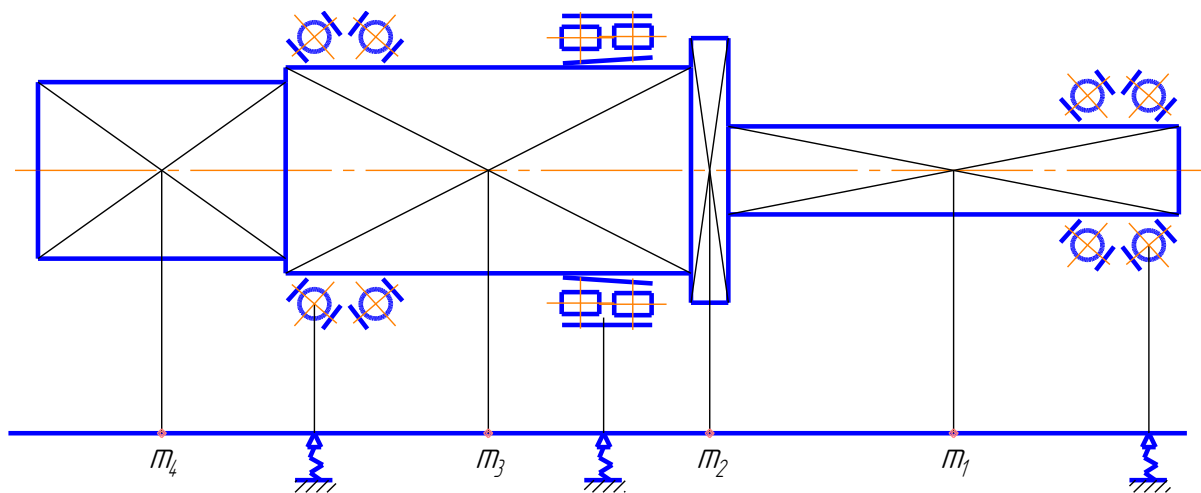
Конструктивна і розрахункова схеми шпиндельного вузла
